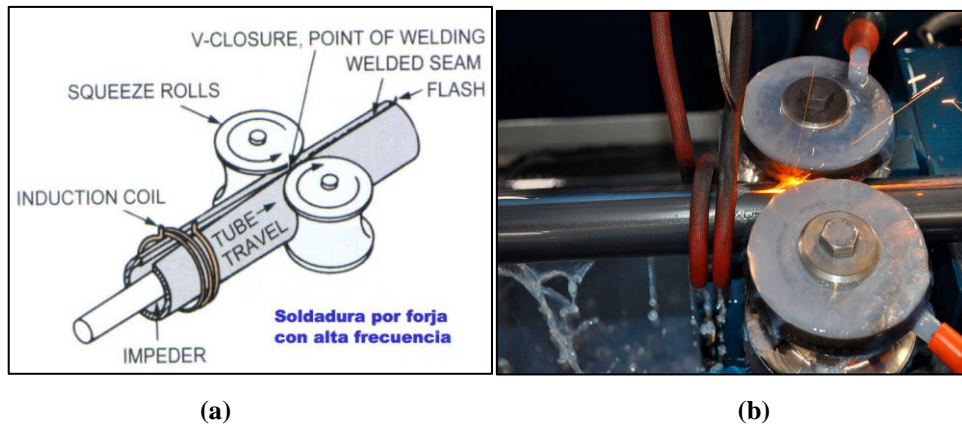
Representación de soldadura por alta frecuencia (a) esquemática, (b) real.
